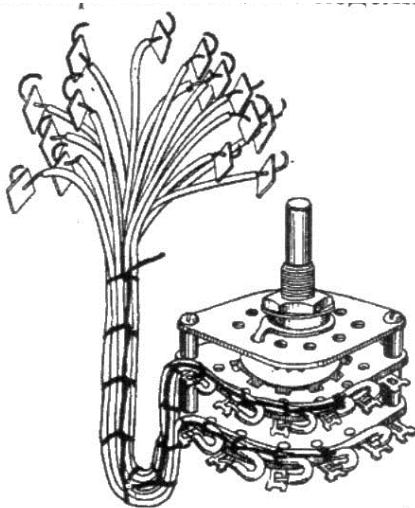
Укладка и вязка монтажных проводов на многоплатном переключателе
